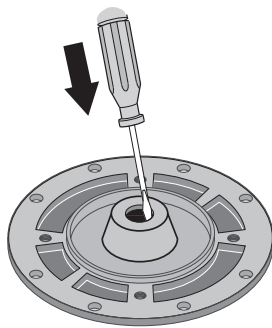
EXTRACCIÓN DE LA JUNTA
